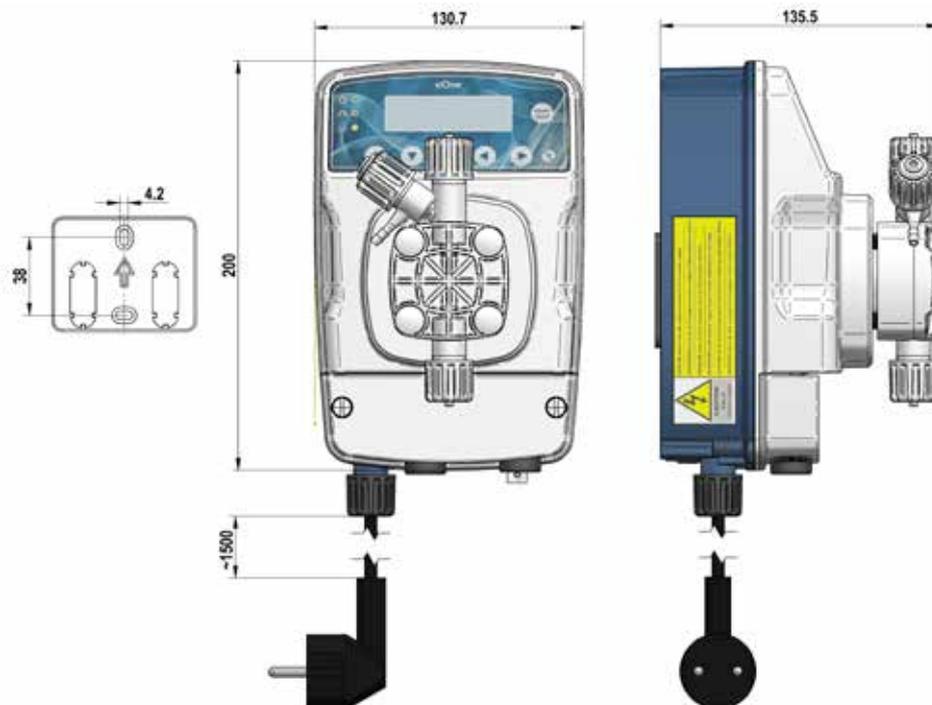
Pompa e Placca per il fissaggio a parete (dimensioni indicate in mm)
